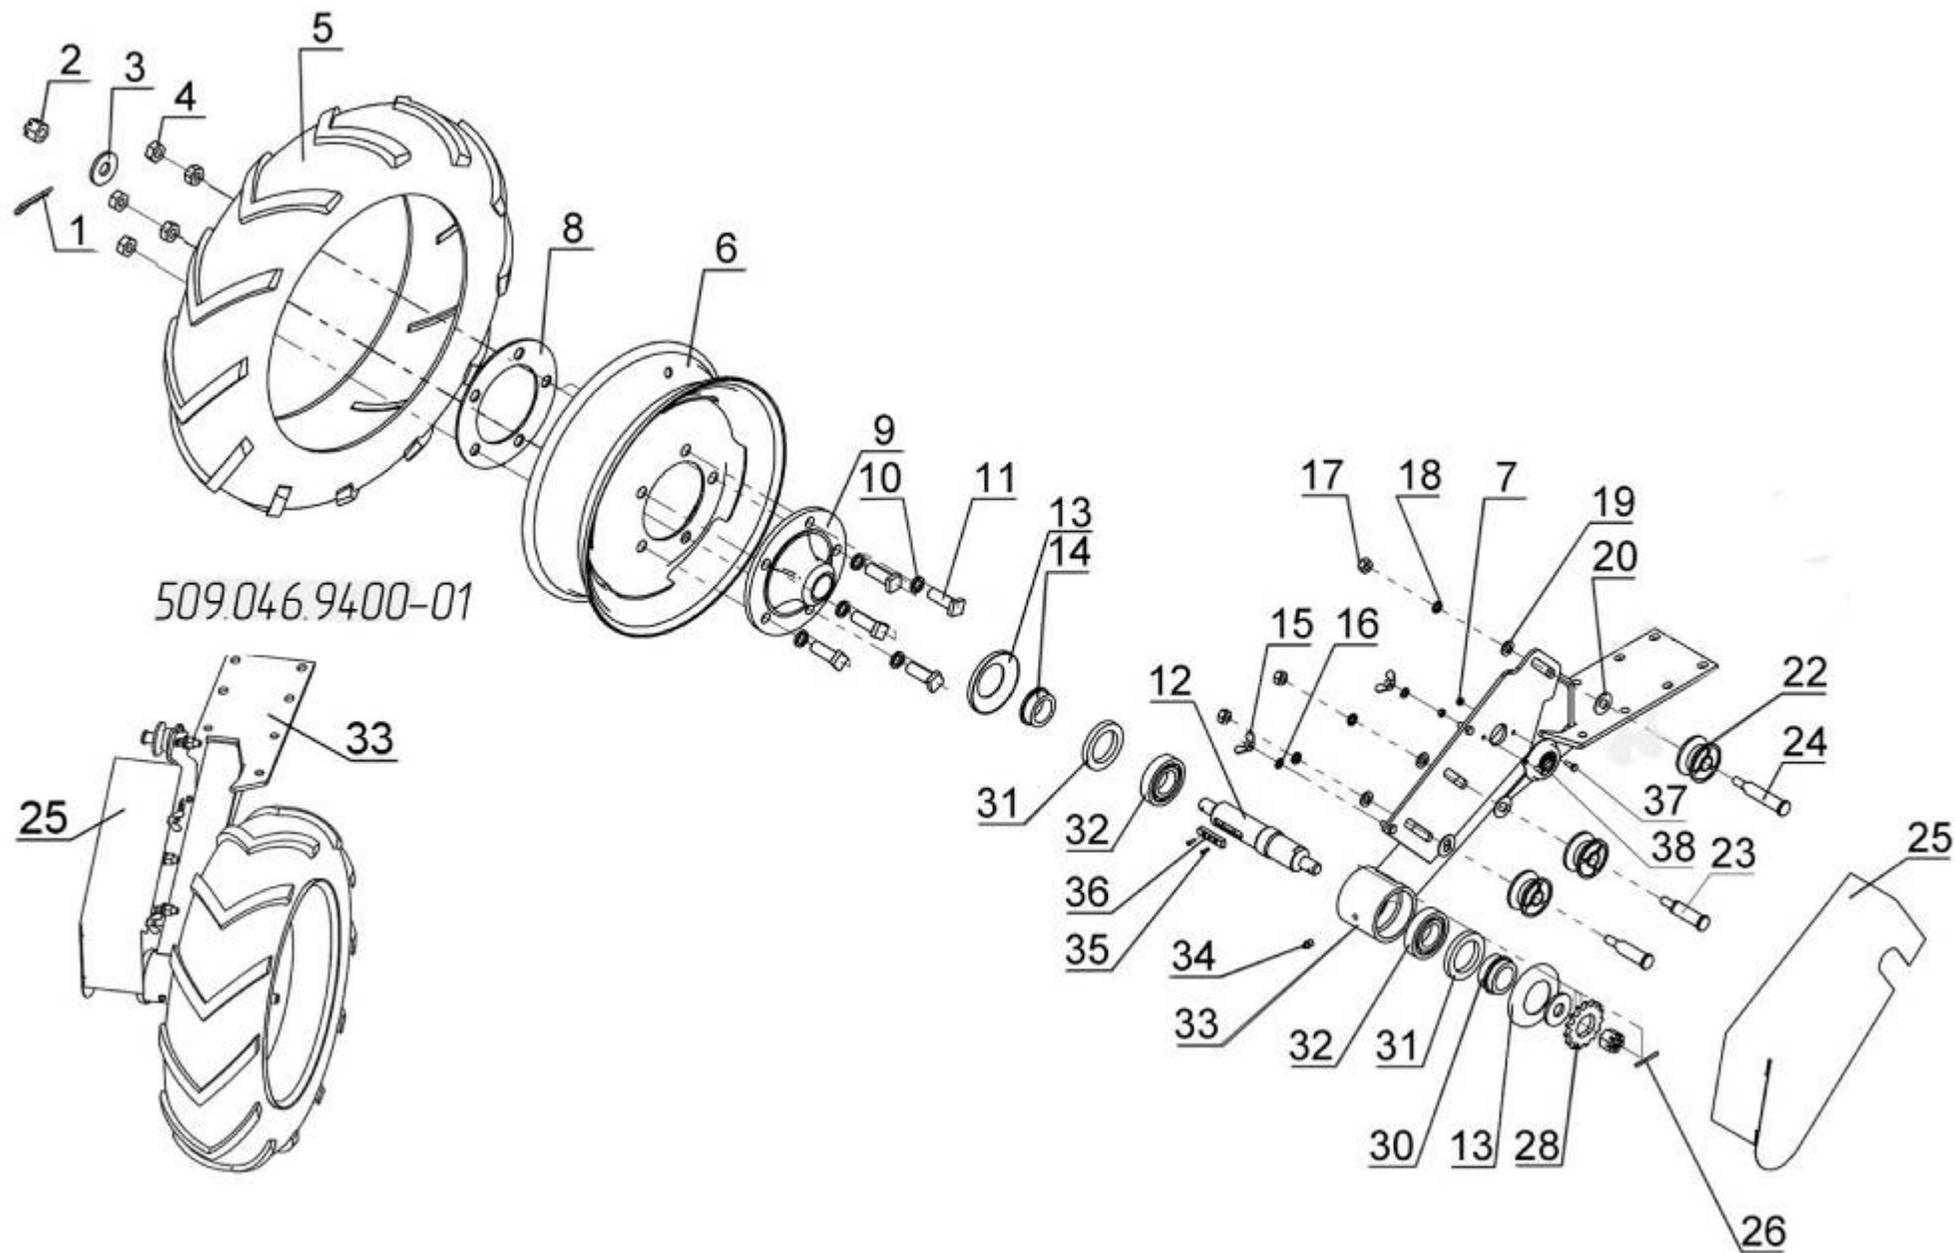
Опорно-приводное колесо 509.046.9400 (левое)
